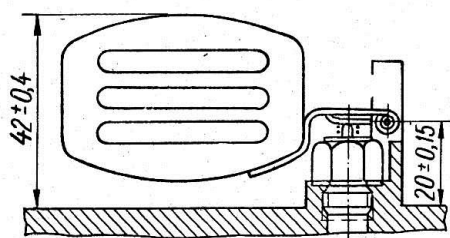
Схема розміщення поплавка в карбюраторі К-126.
